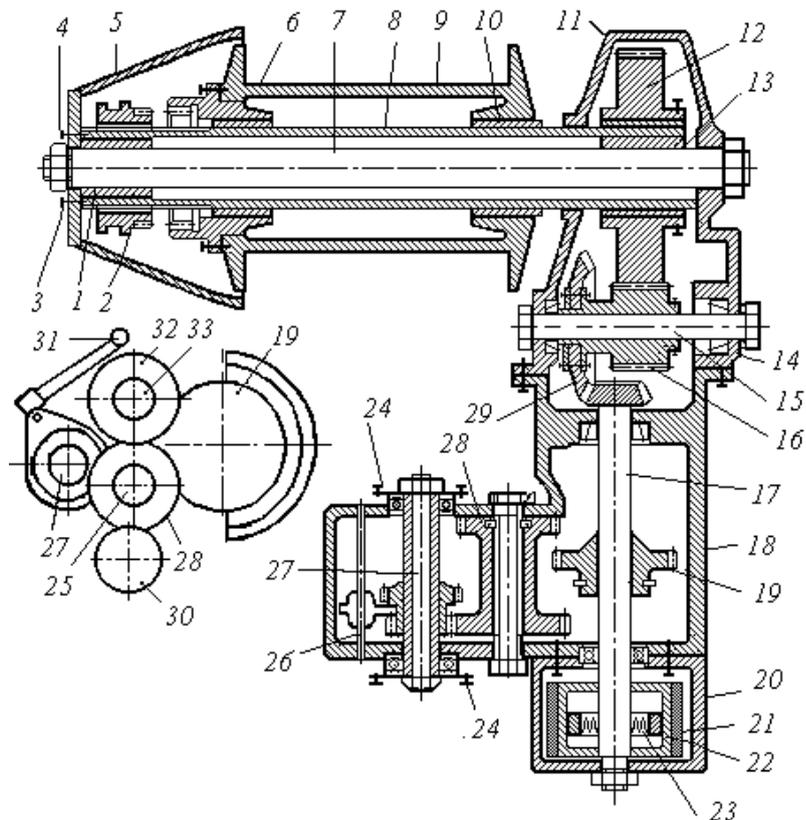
Схема устройства лебедки ТТ-4М: 1, 13 – опорные подшипники трубы; 2 – муфта включения; 3 – болт; 4 – винт установочный; 5 – опора левая; 6, 10 – подшипник барабана; 7 – ось; 8 – труба; 9 – барабан; 11 – крышка редуктора; 12 – колесо зубчатое; 14 – картер редуктора; 15 – вал; 16 – шестерня; 17 – ведущий вал-шестерня; 18 – картер раздаточной коробки; 19 – шестерня реверсивная; 20 – кожух тормоза; 21 – лента тормозная; 22 – шкив; 23 – муфта свободного хода; 24 – вилки карданных валов; 25, 33 – оси; 26 – подвижный блок шестерен; 27 – ведущий вал раздаточной коробки; 28 – блок промежуточных шестерен; 29 – ведомое коническое колесо; 30 – шестерня вала отбора мощности; 31 – рукоятка включения привода; 32 – блок шестерен заднего хода
